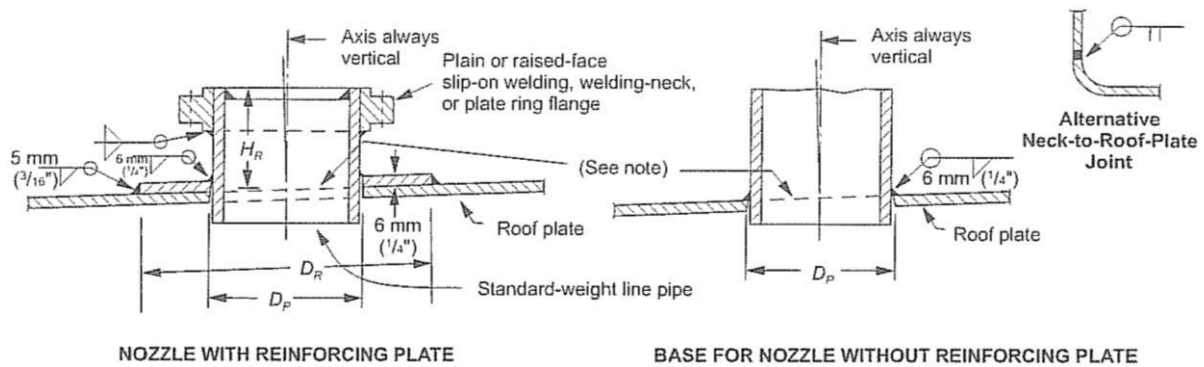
Boquillas con láminas de refuerzo y sin refuerzo
